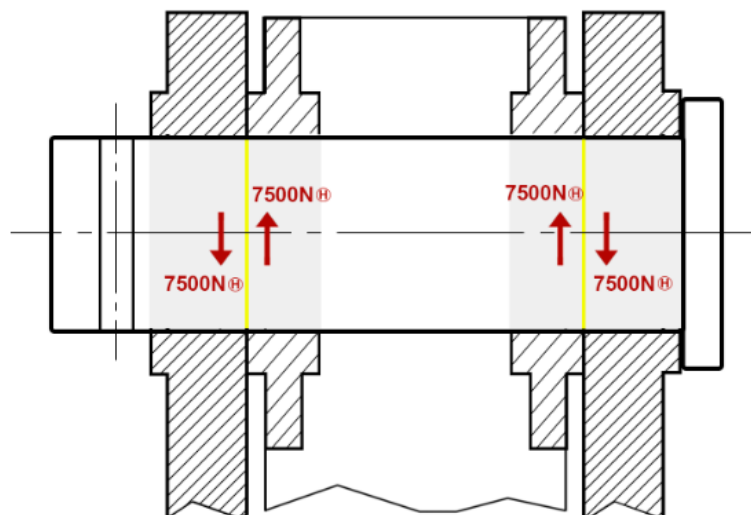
Barra AC-Bancada. SECCIÓN EN PLANTA
